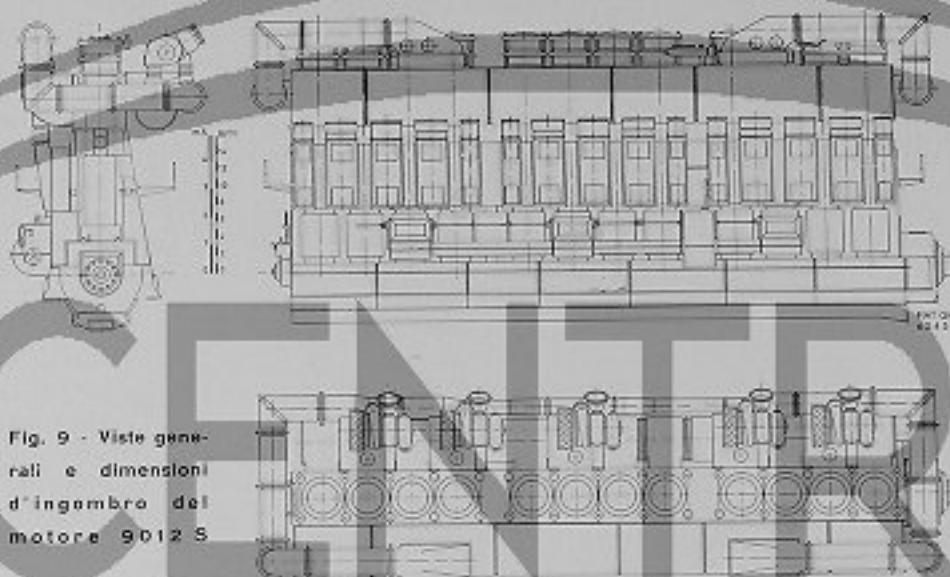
Viste generali e dimensioni d'ingombro del motore 9012 S
